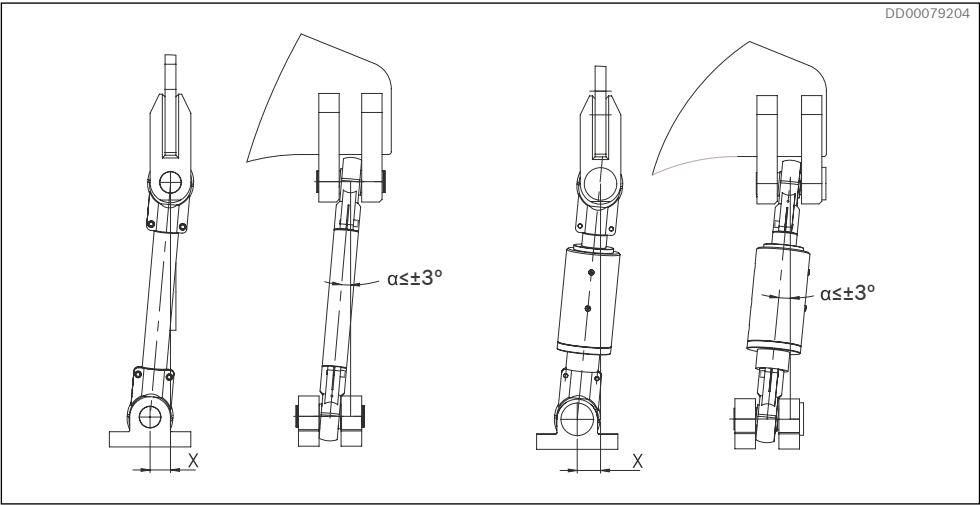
Монтаж шарнирного соединения и гидравлического цилиндра для DTCB
